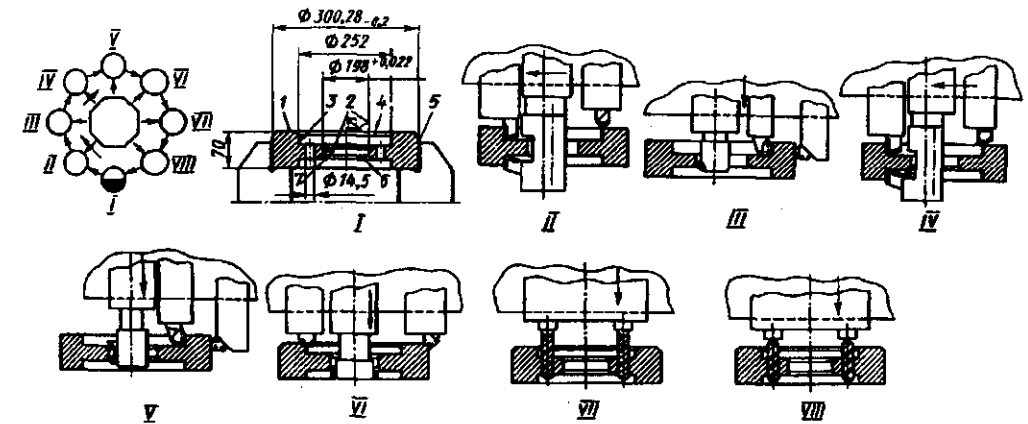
Наладка восьмишпиндельного полуавтомата для обработки заготовок зубчатых колес со сверлением удаленных от центра отверстий
